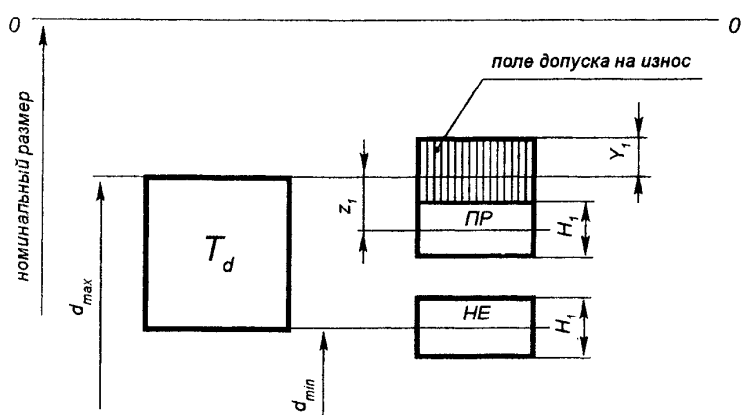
Схема расположения полей допусков калибров для контроля валов изготовленных по квалитетам 6, 7 и 8 при номинальных размерах до 180 мм (для размеров валов изготовленных по квалитетам от 8 до 17, $Y = 0$)
